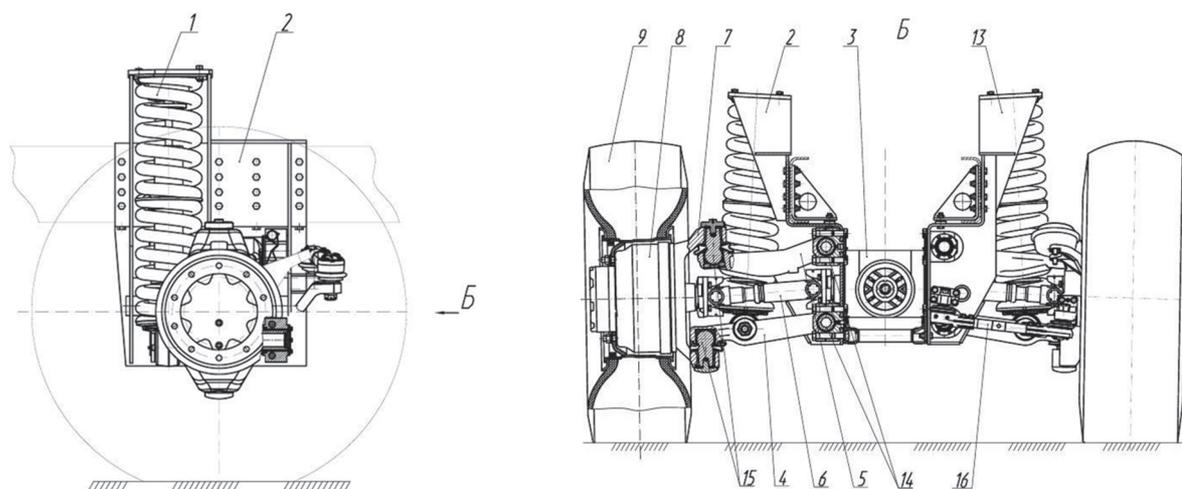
Вариант независимой подвески колес с пружинной рессорой: 1 — амортизаторная стойка; 2, 13 — кронштейны; 3 — центральный редуктор моста; 4 — нижний рычаг; 5 — верхний рычаг; 6 — полуосевой карданный вал; 7 — стойка; 8 — ступица; 9 — колесо; 14, 15 — шарниры; 16 — тяга
